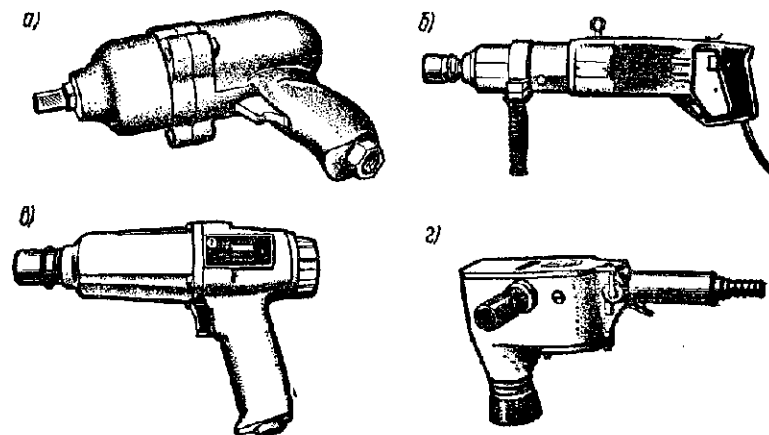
Механизированные гайковерты для разборки резьбовых соединений:
